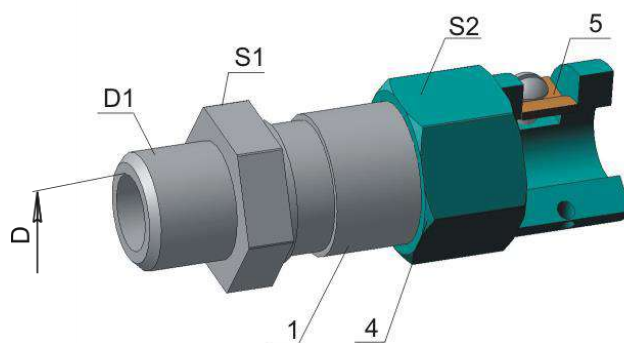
Конструкция кабельного ввода для монтажа кабеля без дополнительной защиты
